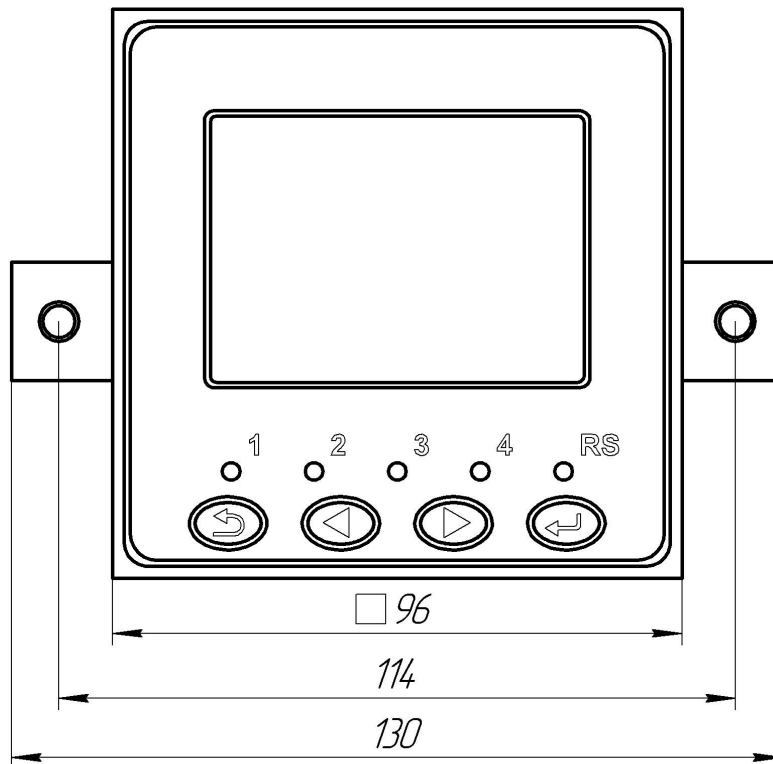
Габаритные размеры корпуса измерительного прибора (ИП)
